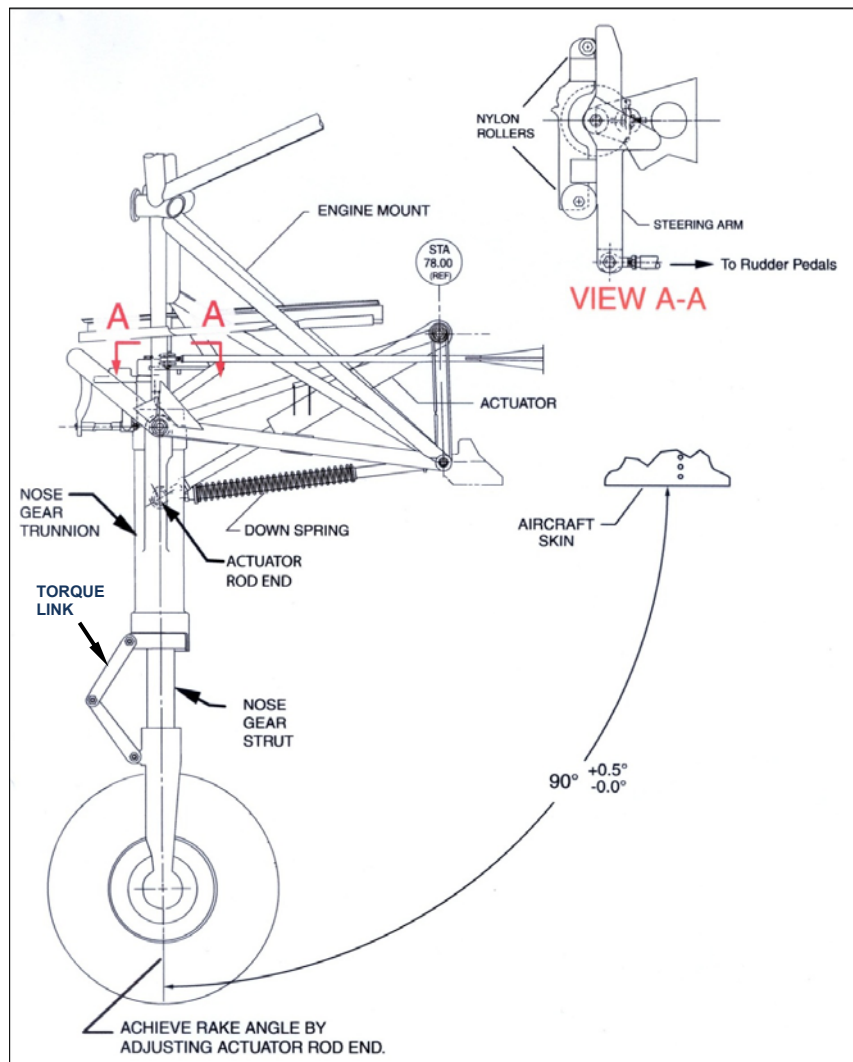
Train d'atterrissage avant du Piper PA46-500TP, vue de la gauche
